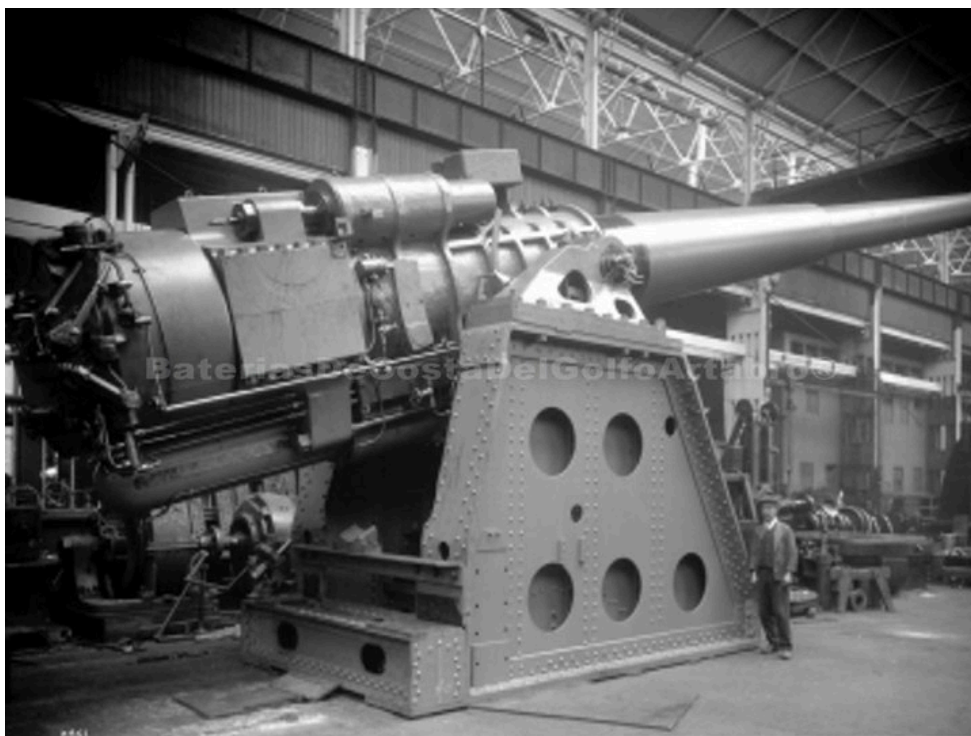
Vista de un cañón Vickers en proceso de fabricación.
